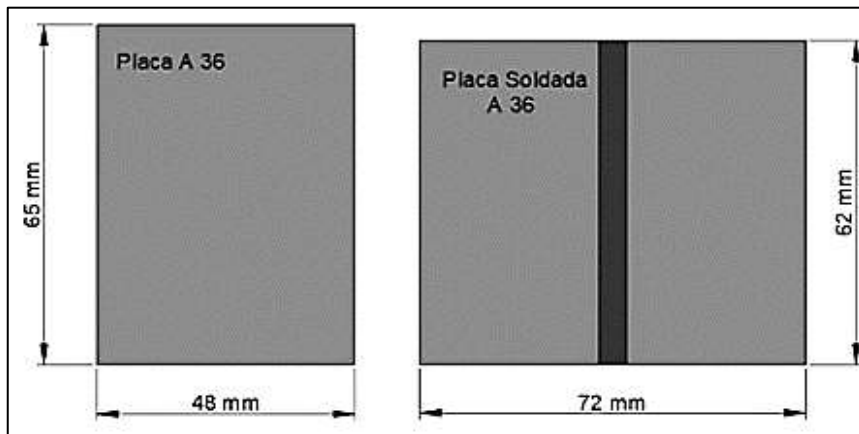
Dimensiones de las placas y juntas soldadas de acero A-36
